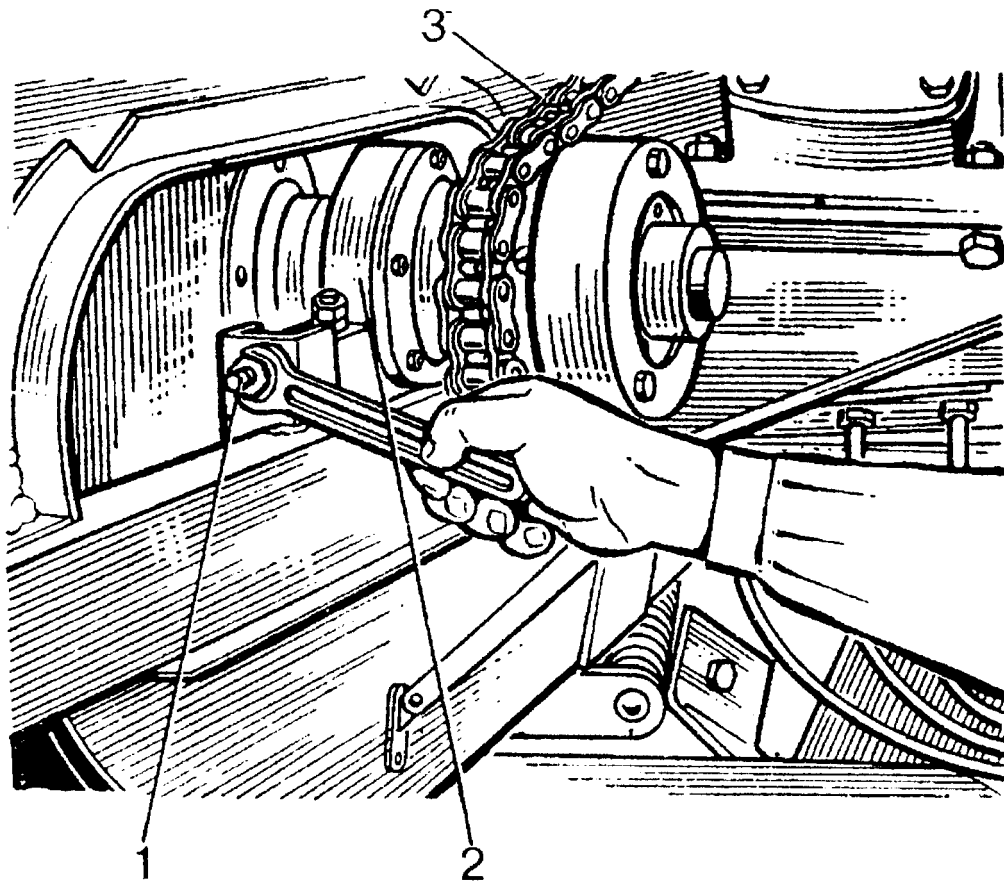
Регулировка цепи привода очесывающего барабана:
